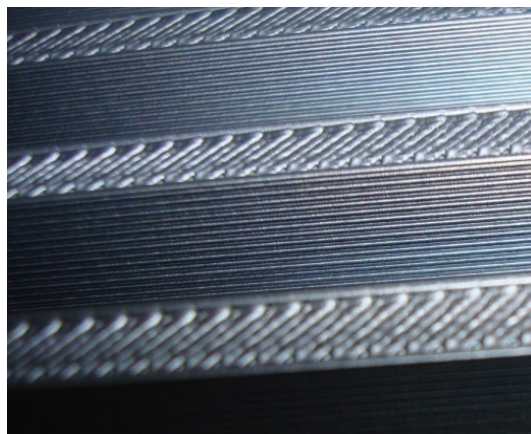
Zobrazení procesu tisku na Dimension SST 768
